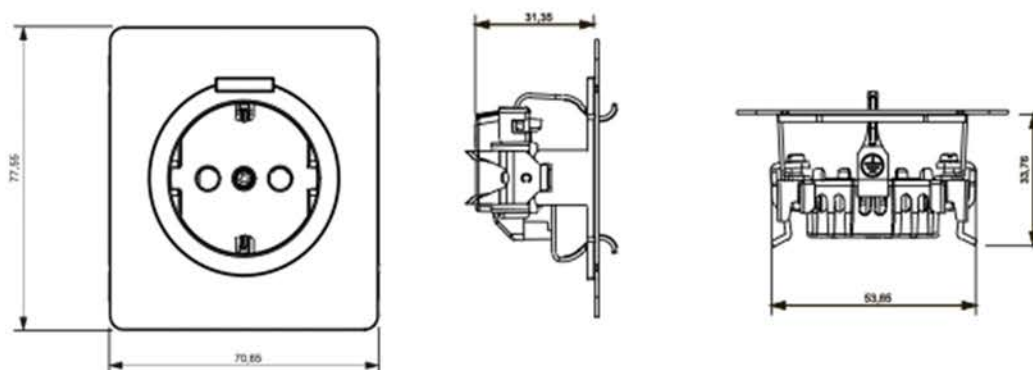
Габаритные и установочные размеры розетки / Figure 2 – Overall and mounting dimensions of socket / 2-сурет – Розетканың габариттік және орнату өлшемдері
